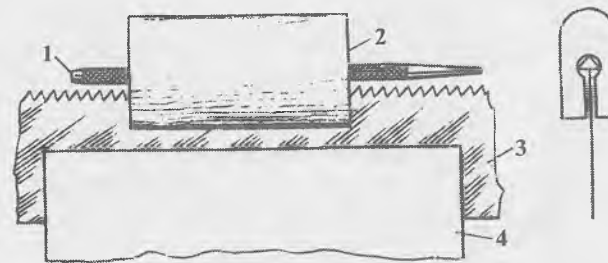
Приспособление для фугования зубьев напильником: 1 — напильник; 2 — колодка; 3 — полотно пилы; 4 — тиски
